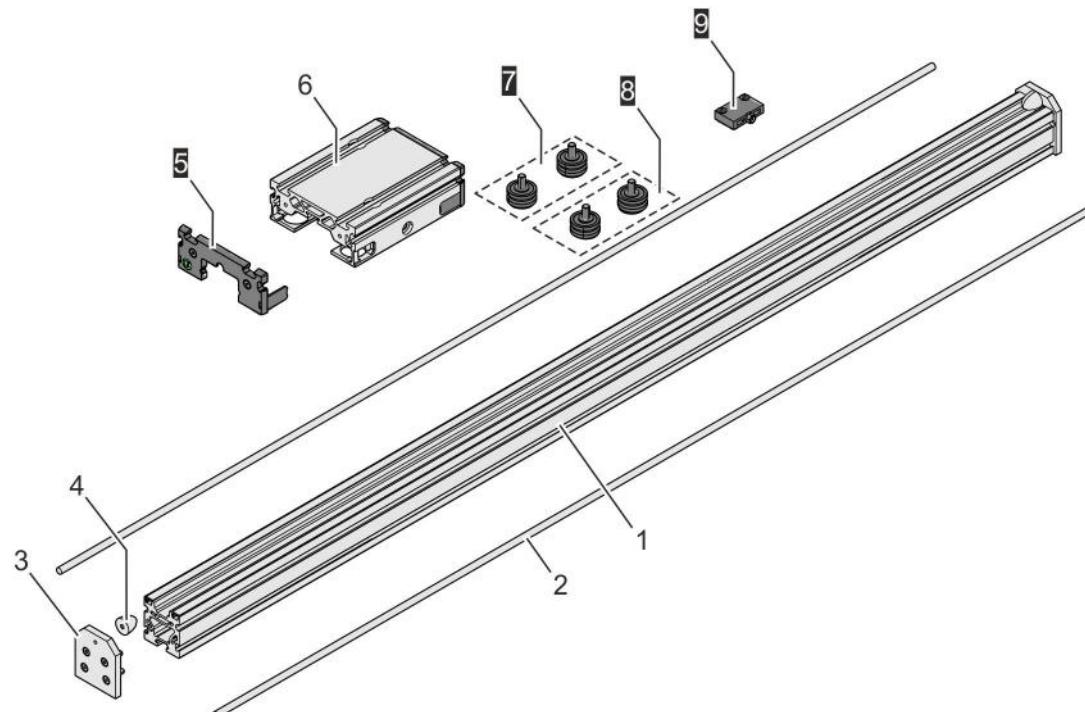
Unité linéaire RK MonoLine R – vue éclatée
